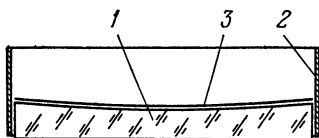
Форма для отливки шлифовальника и полировальника (разрез). 1 — основание формы (будущее зеркало), 2 — картонный бортик, 3 — бумажный круг.
